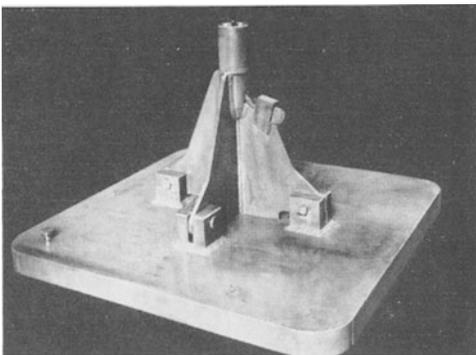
Ausbildung des Stampfkörpers als Platte (Aufnahme MENCK & HAMBROCK).
